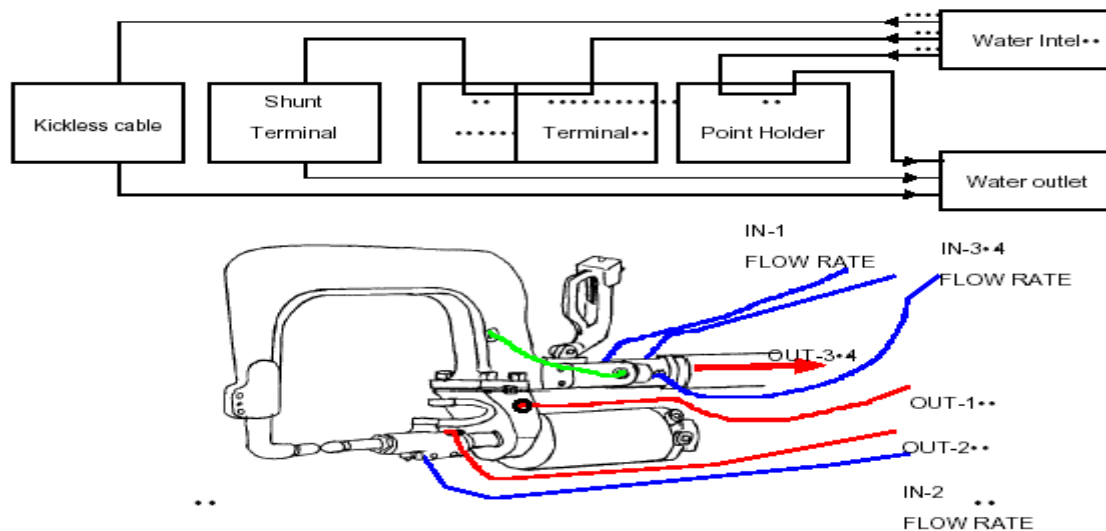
Estándar para una soldadora tipo C.
